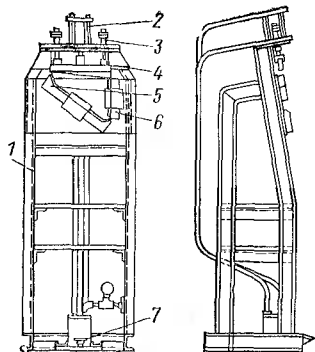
Стенд для запрессовки стекол дверей автомобилей
